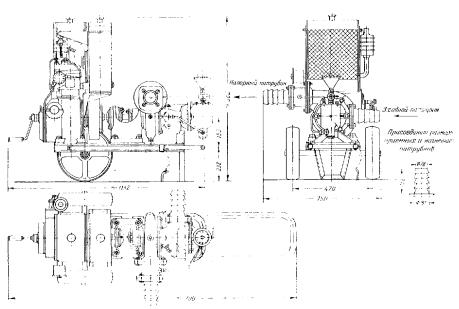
Габаритный чертеж мотопомпы модели БМП-80а
